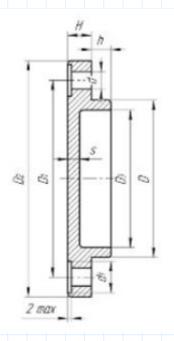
Конструкция мазеудерживающего кольца, подшипниковые узлы с использованием пластичного смазочного материала
